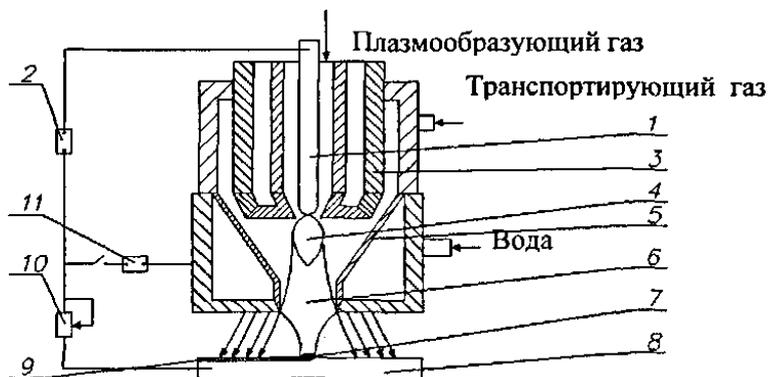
Схема плазменной наплавки с вдуванием порошка в дугу: 1 – неплавящийся электрод; 2 – источник питания; 3 – сопло; 4 – плазменная струя; 5 – сопло; 6 – сжатая дуга; 7 – сварочная ванна; 8 – основной металл; 9 – наплавленный металл; 10 – балластный реостат; 11 – резистор
